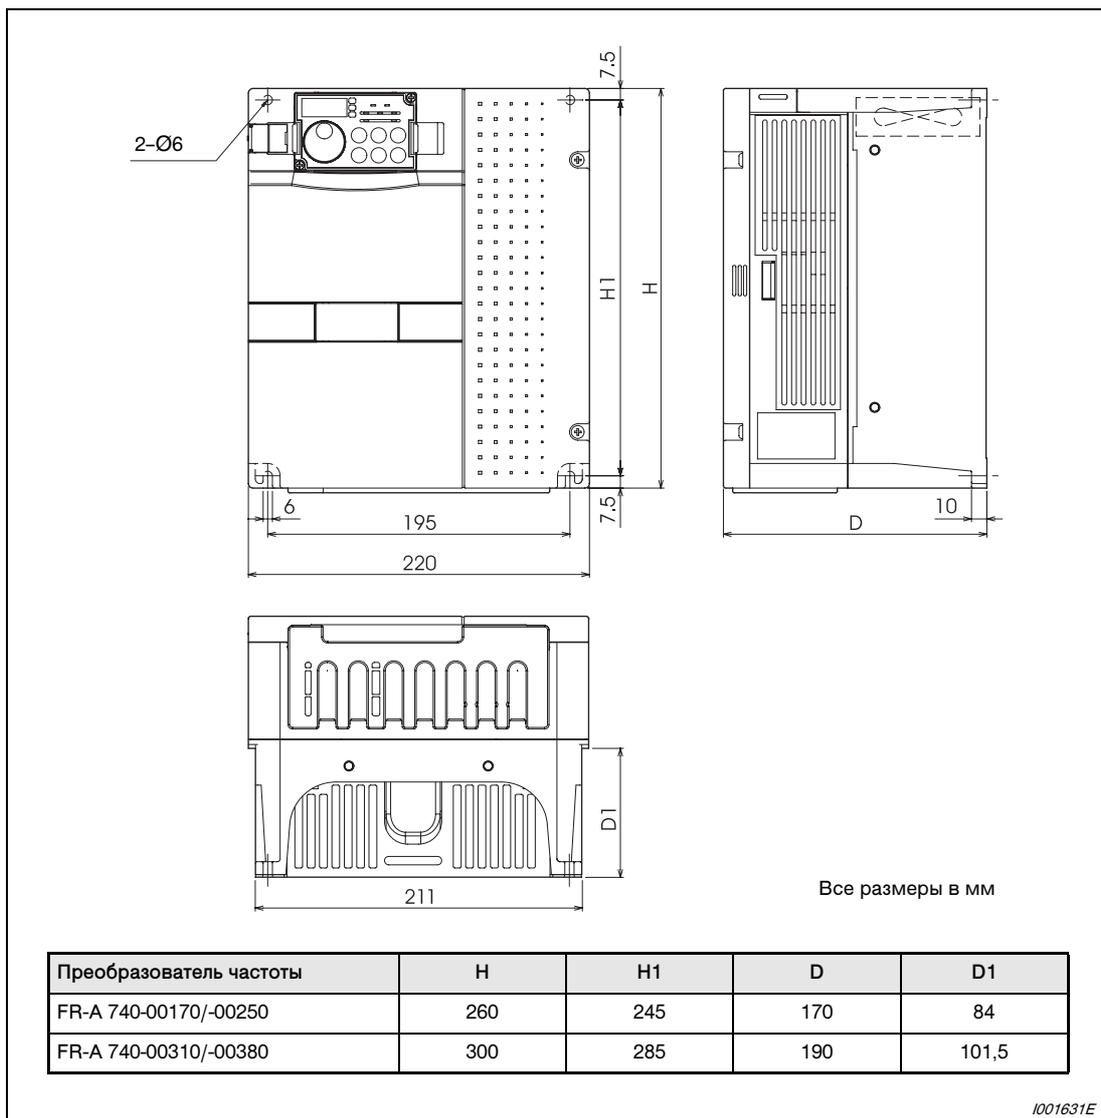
Размеры FR-A 740-00170 ... -00380
